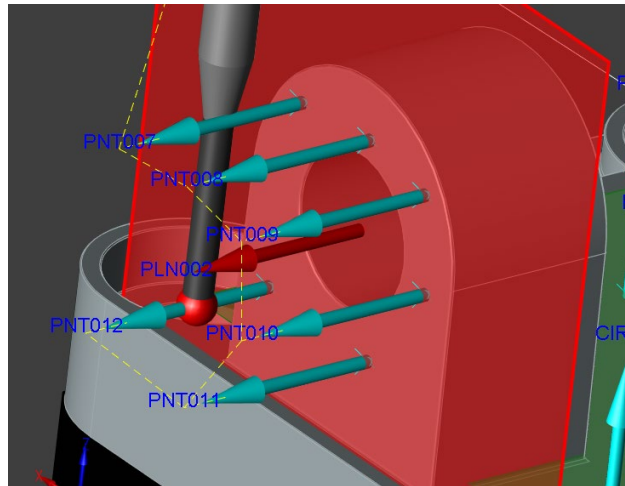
Construcción de un plano con 6 puntos palpados
